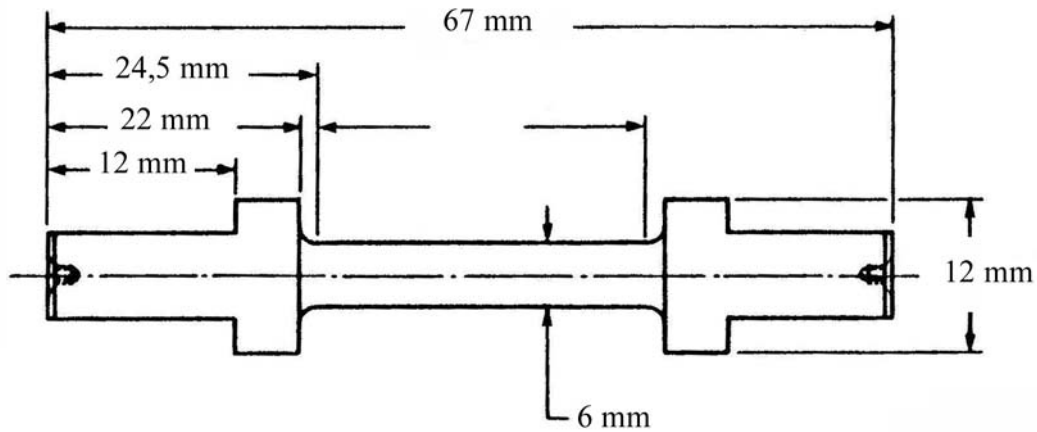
Esquema de sección longitudinal y transversal de las probetas de torsión empleadas en el presente trabajo.
